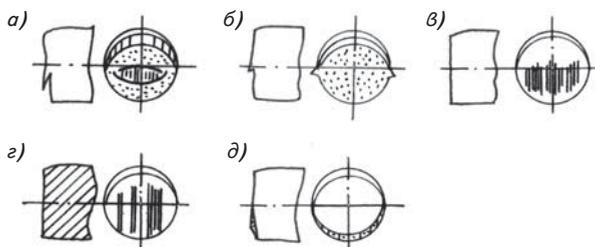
Неоднородности и возможные дефекты на торцах заготовок, отрезанных сдвигом: а, б — заусенцы (а — торцовый; б — боковой); в — пригар; з — наплыв; д — задиры
